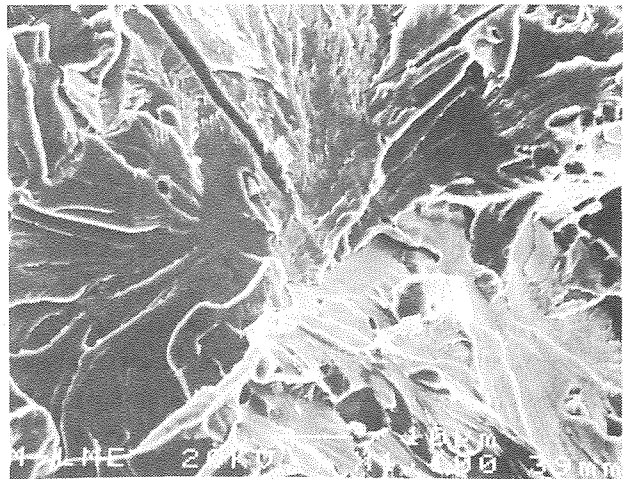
Zona de iniciación de la fractura frágil en una probeta Charpy V rota a -40°C .
